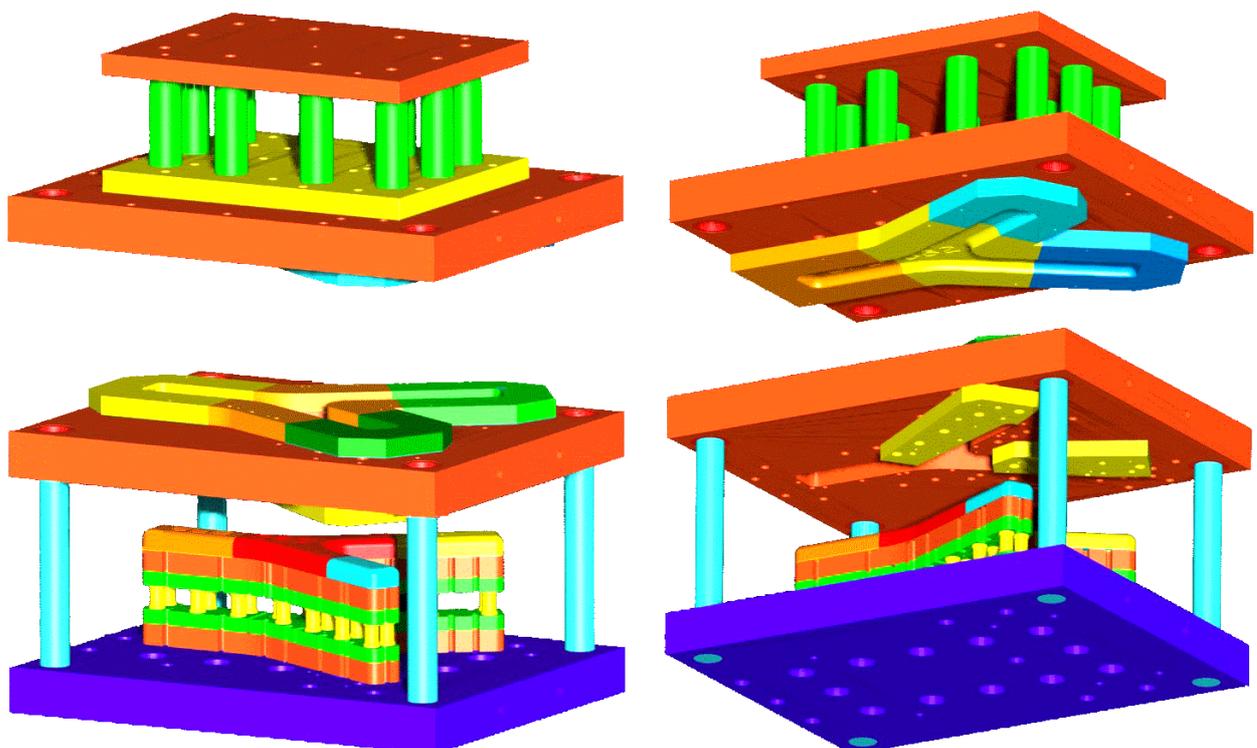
CAD-Modell des Tiefziehwerkzeugs (Pro/ENGINEER)
